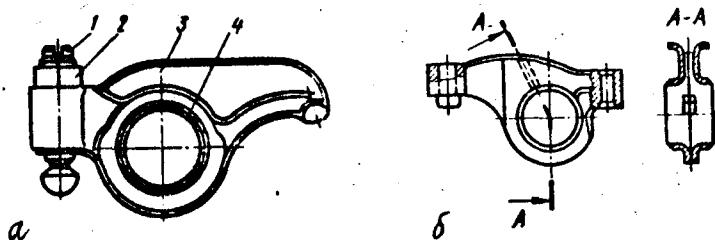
Коромисла: а – литі; б – штамповані; 1 – регулювальний болт; 2 – контргайка; 3 – коромисло; 4 – підшипникова втулка
